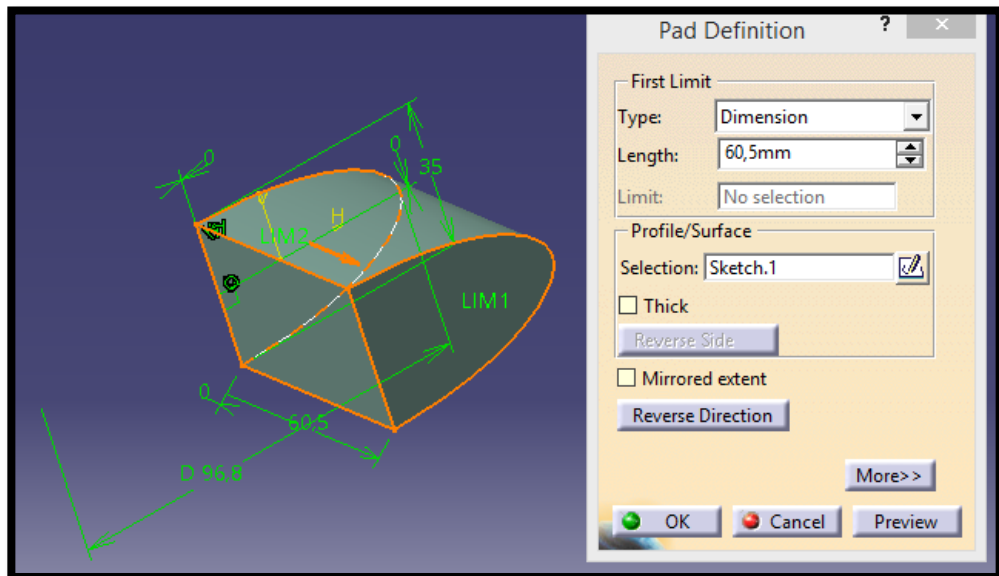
Seat mounting frame 11: Pad pestillo 1
